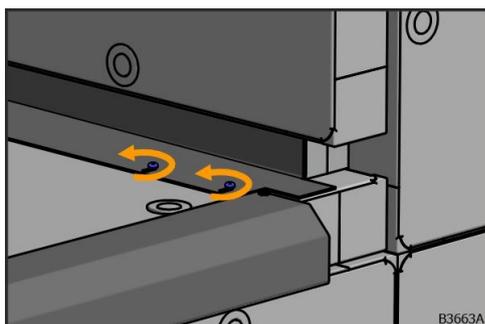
desserrage des vis de raccordement de la cornière d'étanchéité
